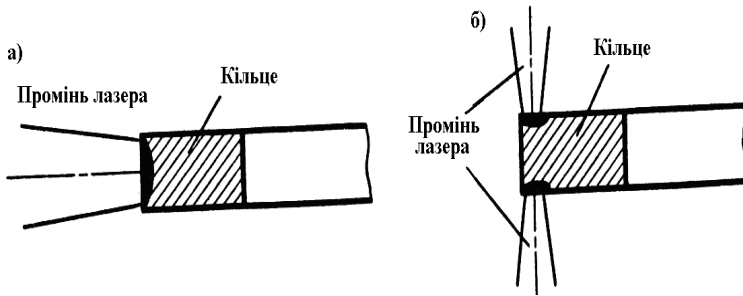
Зміцнення поршневих кілець по боковій циліндровій поверхні (а) і по торцевих поверхнях (б)
